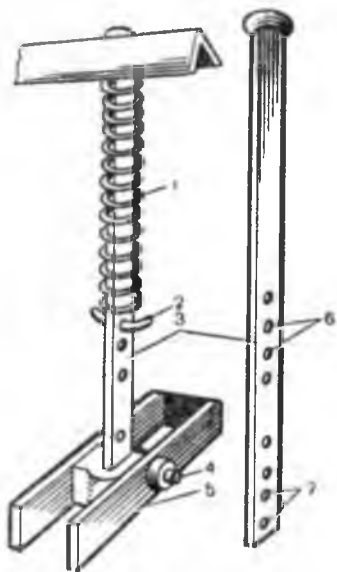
Регулировка коротких и односторонних грядилей культиватора КПС-4:
